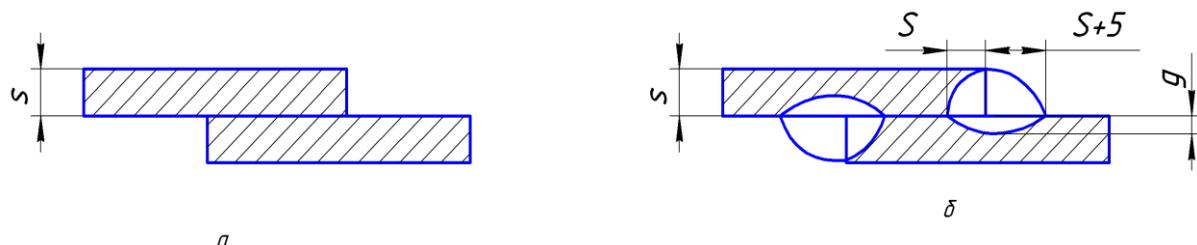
Сварное соединение до (а) и после сварки (б)
